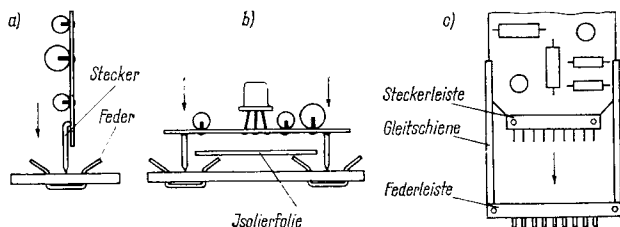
Amateurlösungen für Baugruppenanschlüsse
